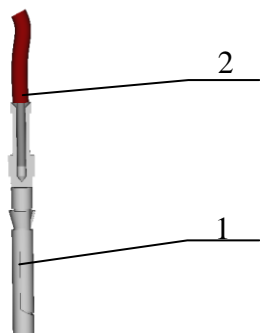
Инструмент монтажный для демонтажа контактов 09990000052
